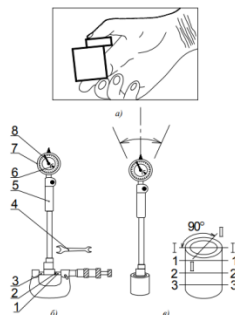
Схема измерения действительных размеров втулки нутромером с индикатором часового типа: а – схема притирки блока концевых мер; б – настройка нутромера; в – схема измерения действительных размеров втулки; 1, 3 – стержни измерительные нутромера; 2 – контргайка; 4 – ключ; 5 – ручка деревянная нутромера; 6 – стрелка индикатора малая; 7 – кольцо; 8 – стрелка индикатора большая.
